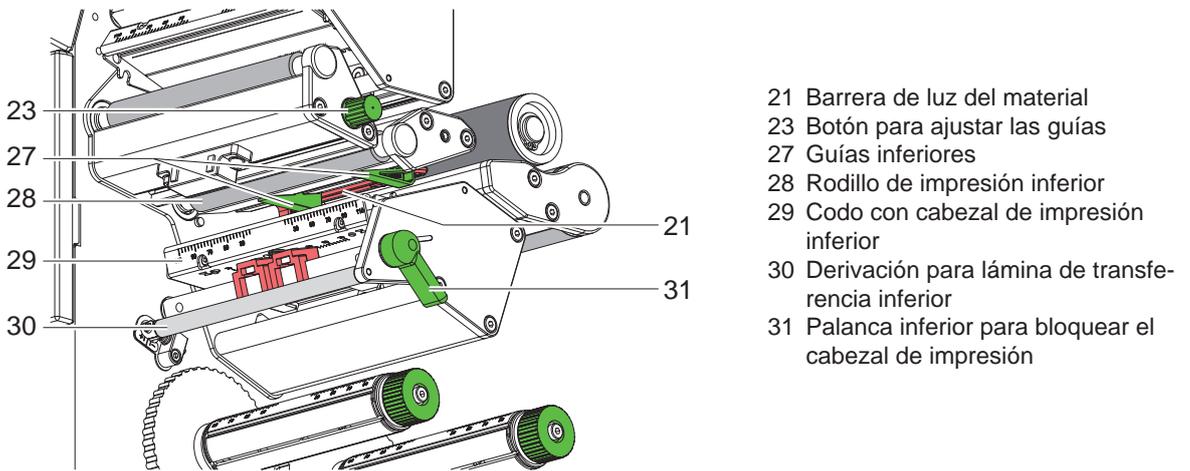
Mecanismo de impresión - módulo inferior de impresión
